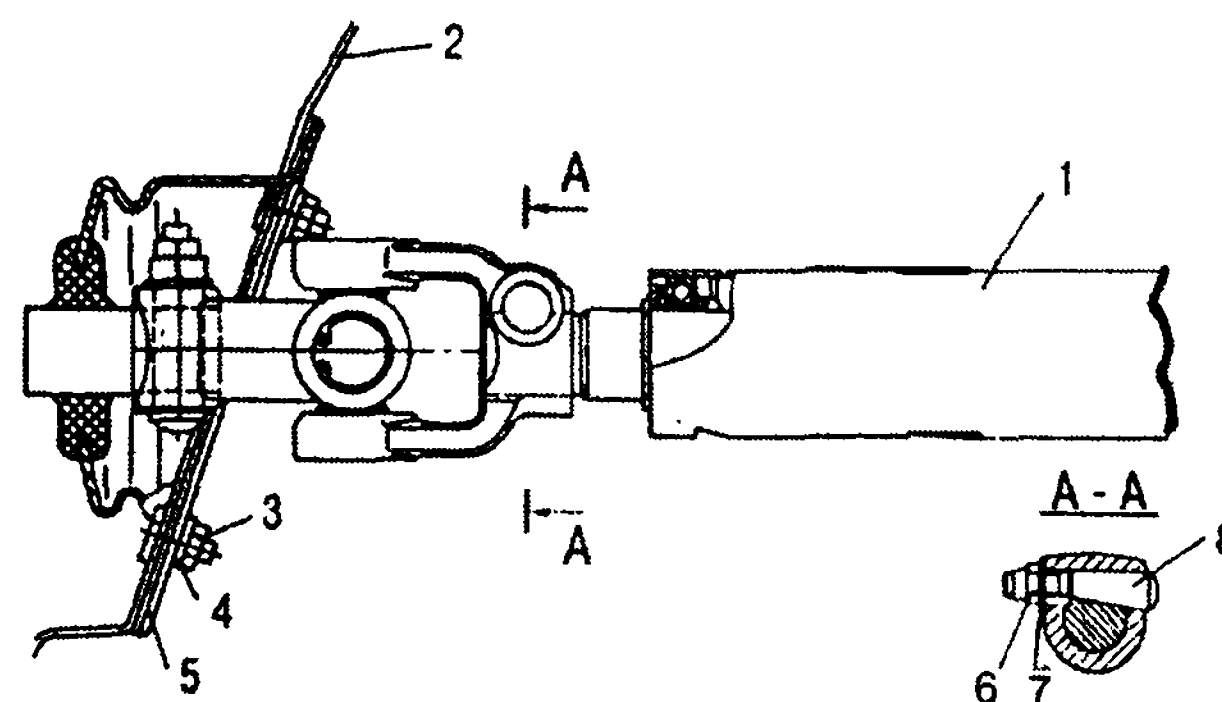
Снятие рулевого механизма с автомобиля: 1 - колонка рулевого механизма в сборе; 2 - щиток передка; 3 - гайка; 4 - шайба; 5 - держатель (кольцо); 6 - шайба; 7 - гайка; 8 - клин
